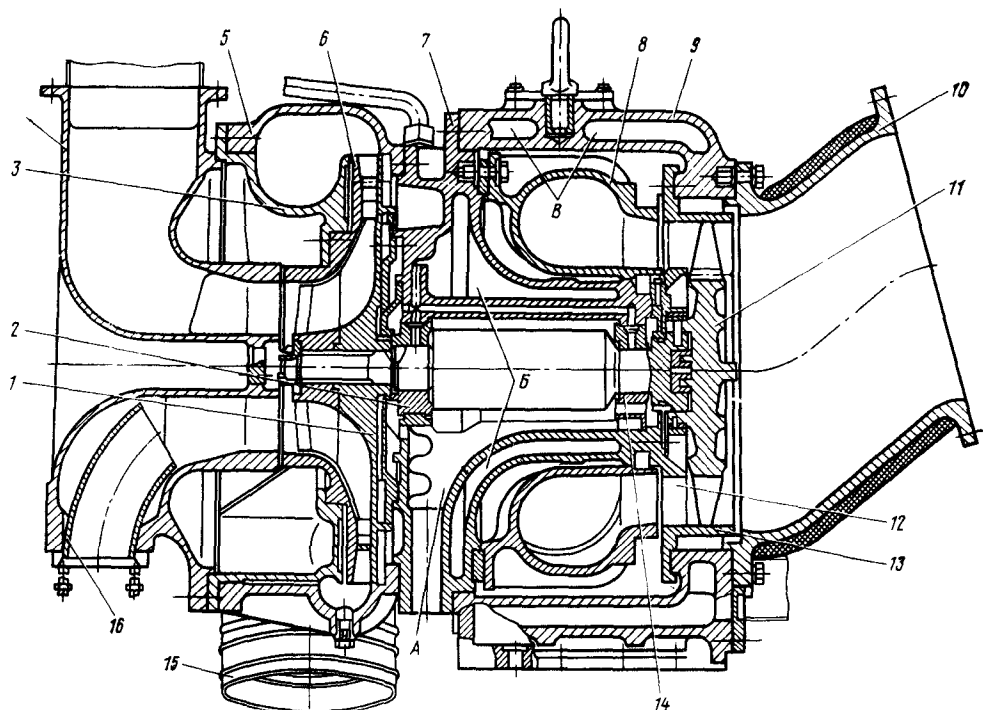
Продольный разрез турбокомпрессора дизеля 2А-5Д49:
